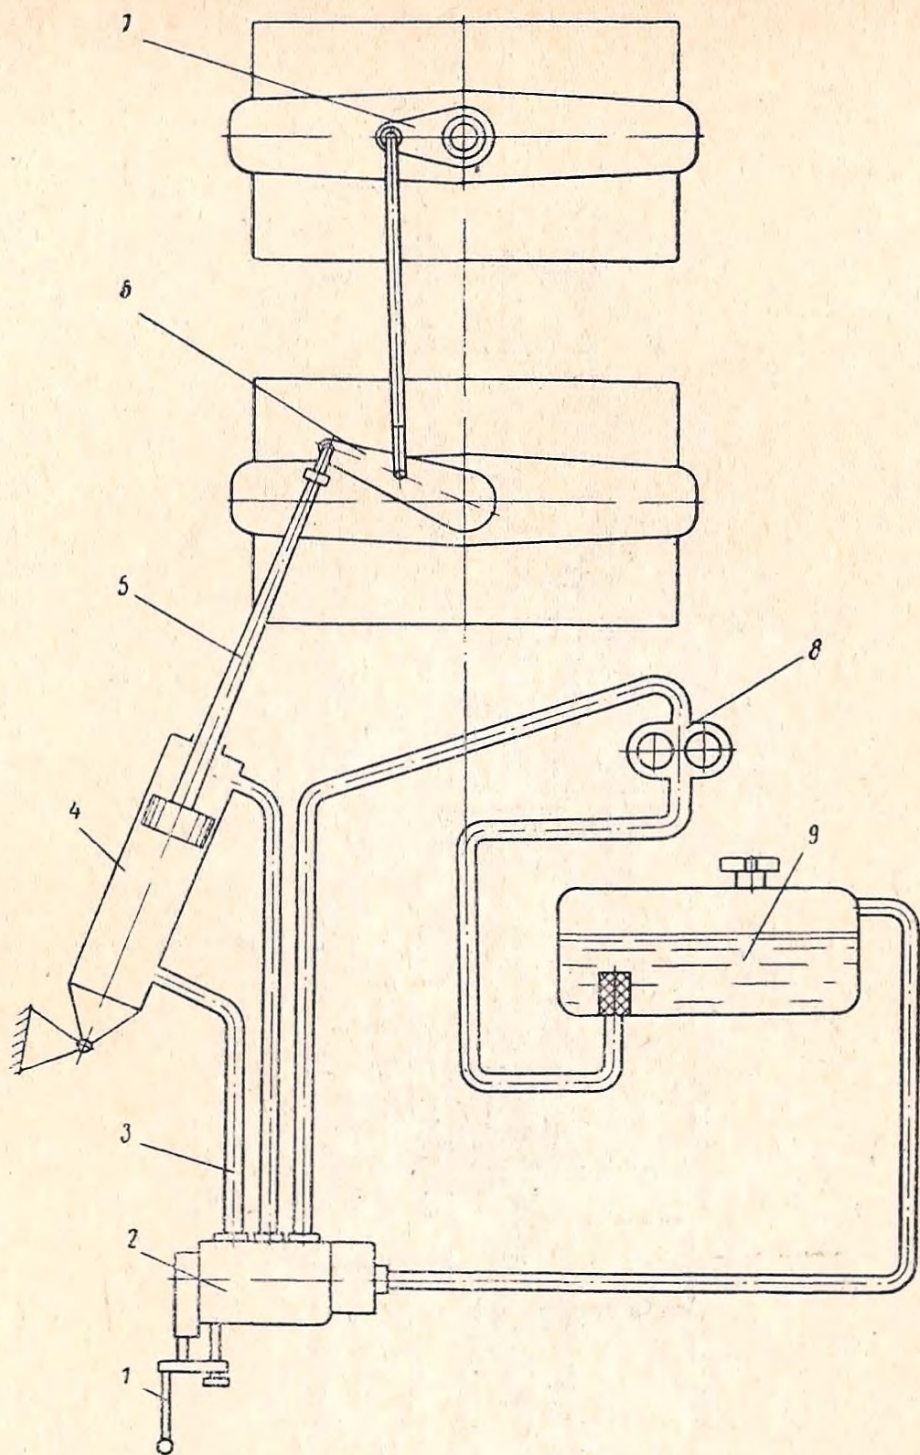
Гидравлическая схема управления поворотом моторного катка Д-400А:
